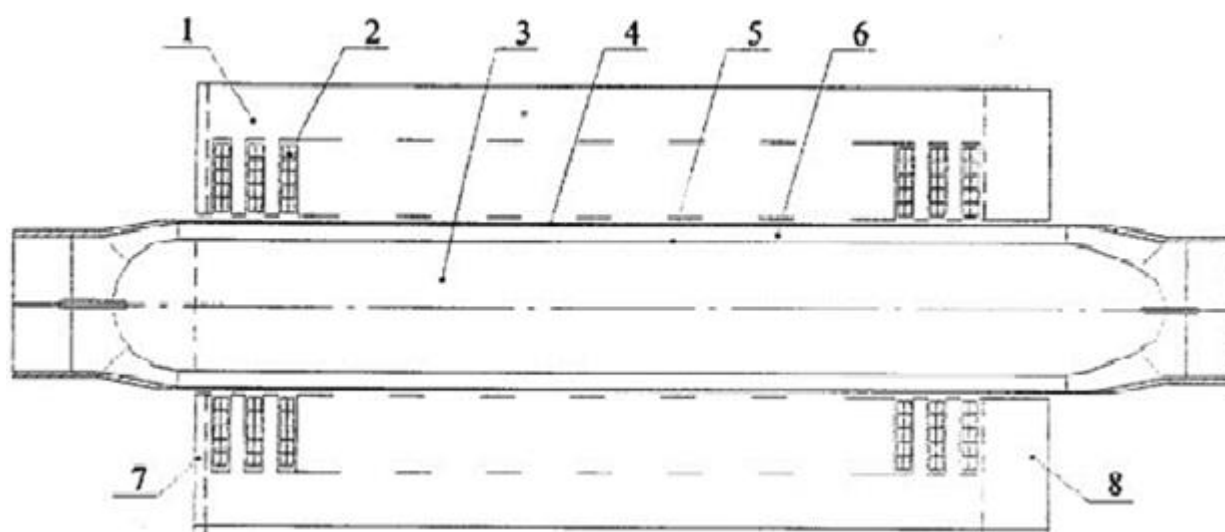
Цилиндрический линейный индукционный насос
